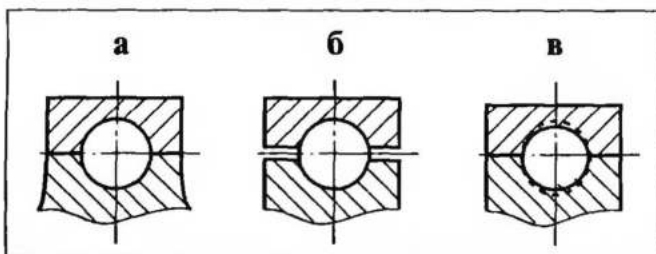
Общая схема ремонта "разъемных" отверстий: а — отверстие до ремонта; б — обработка поверхностей разъема; в — эллипсность отверстия после соединения деталей: (---) — контур отверстия после ремонта
